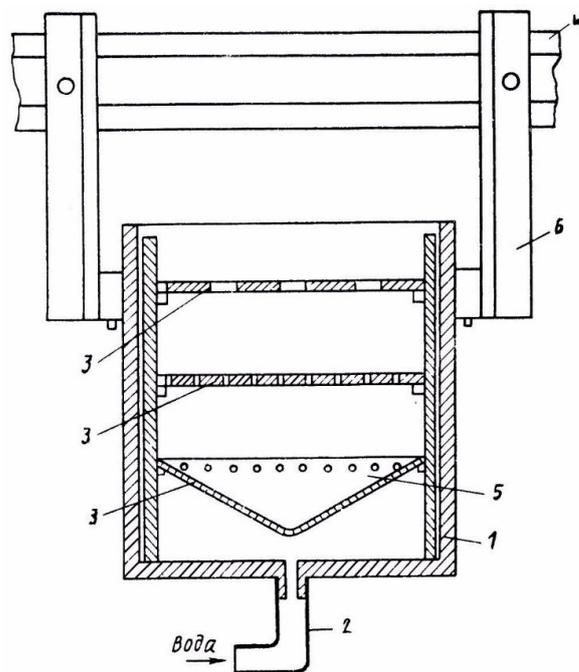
Чертеж устройства для пофракционного отбора шлама в процессе бурения: 1 – корпус прибора; 2 – патрубок для подачи воды; 3 – блок решеток с последовательно установленными по высоте секциями; 4 – шламоотделитель; 5 – поддон воронкообразной формы; 6 – рама жесткой связи
